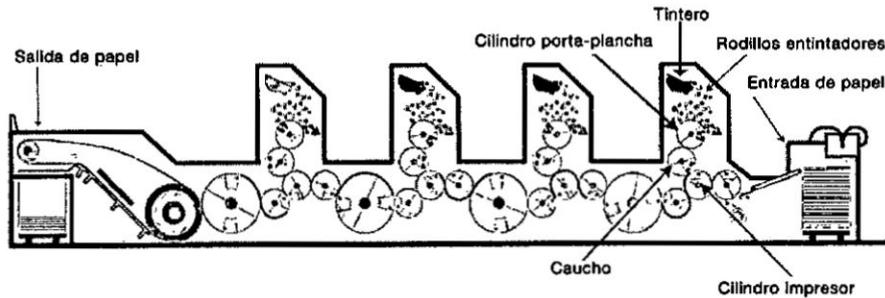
Sistema de rodillos y engranajes de una máquina impresora offset.
